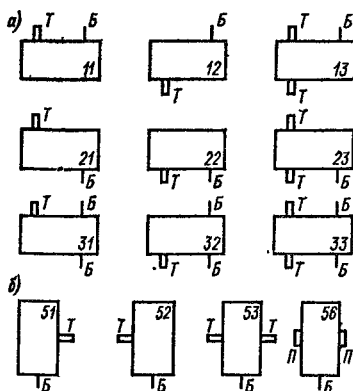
Варианты схем сборок редукторов: а — зубчатые редукторы (в редукторах Ц2 предусмотрены все девять схем сборок, а также по шесть схем сборок с концами тихоходных валов для присоединения командоаппарата, а в редукторах ВКУ-М — сборки 12, 13, 21, 23, 33); б — червячные редукторы 2Ч; Б — конец быстроходного вала; Т — конец тихоходного вала; П — тихоходный вал полый
